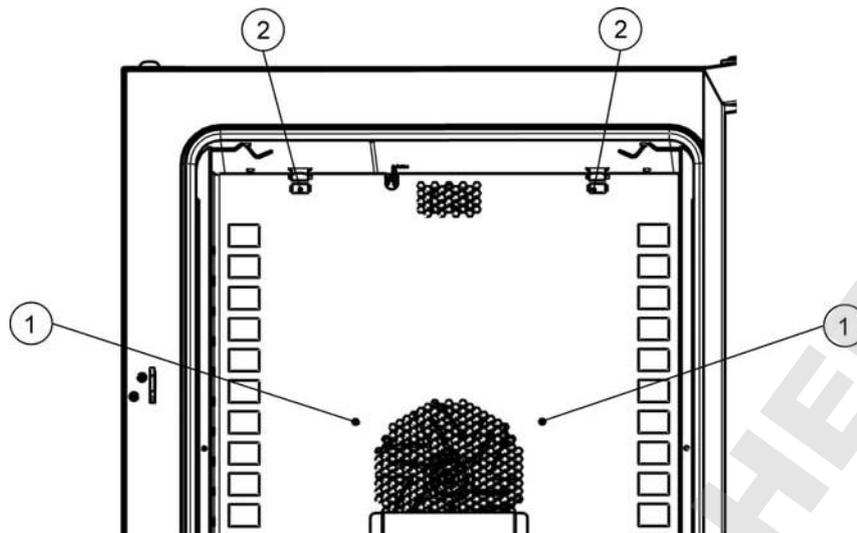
Installation du déflecteur d'air de la paroi arrière
